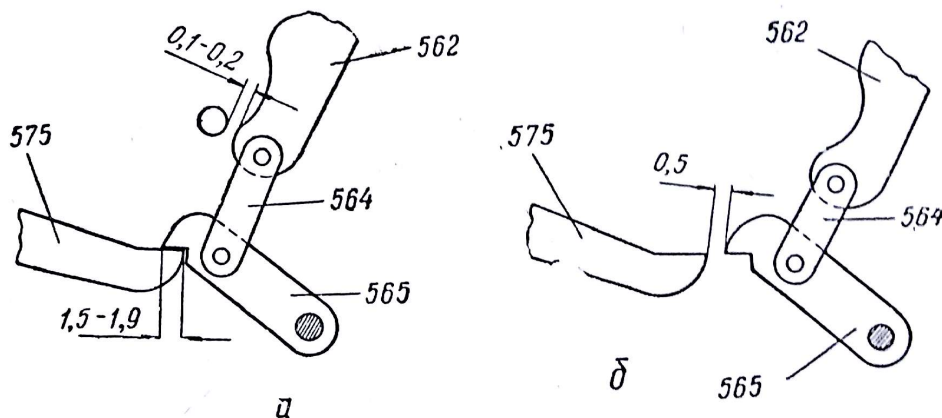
Взаимодействие стопорного рычага 565 с зубом установочного барабана:
